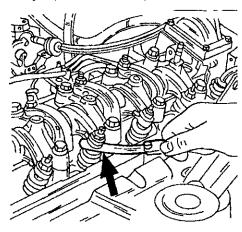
Вставить щуп в указанную стрелками щель между концом стержня клапана и регулировочным винтом. Момент затяжки контргайки 18 нм (двигатели типа TU),
